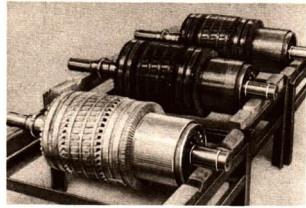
/1 Trommelanker technischer Gleichstrommaschinen
